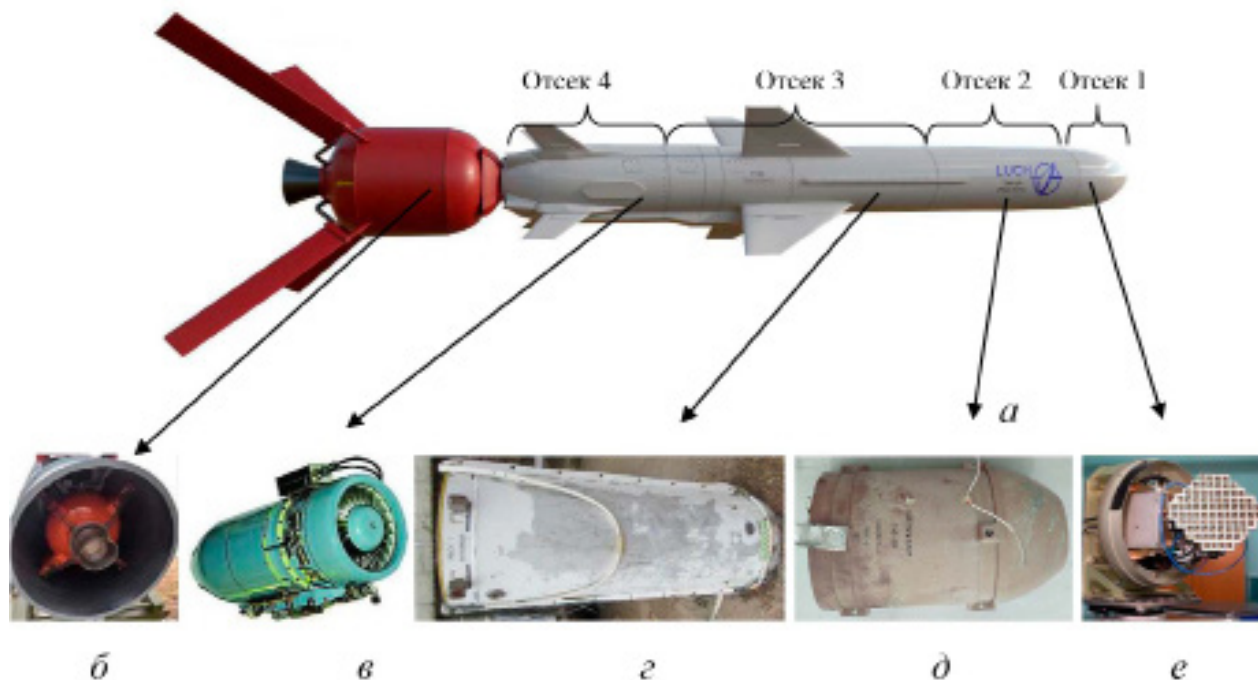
Компоновка ракеты Р-360: а – общий вид, б – стартовая ступень, в – двигатель МС-400, г – топливный бак, д – боевая часть, е – ГСН
